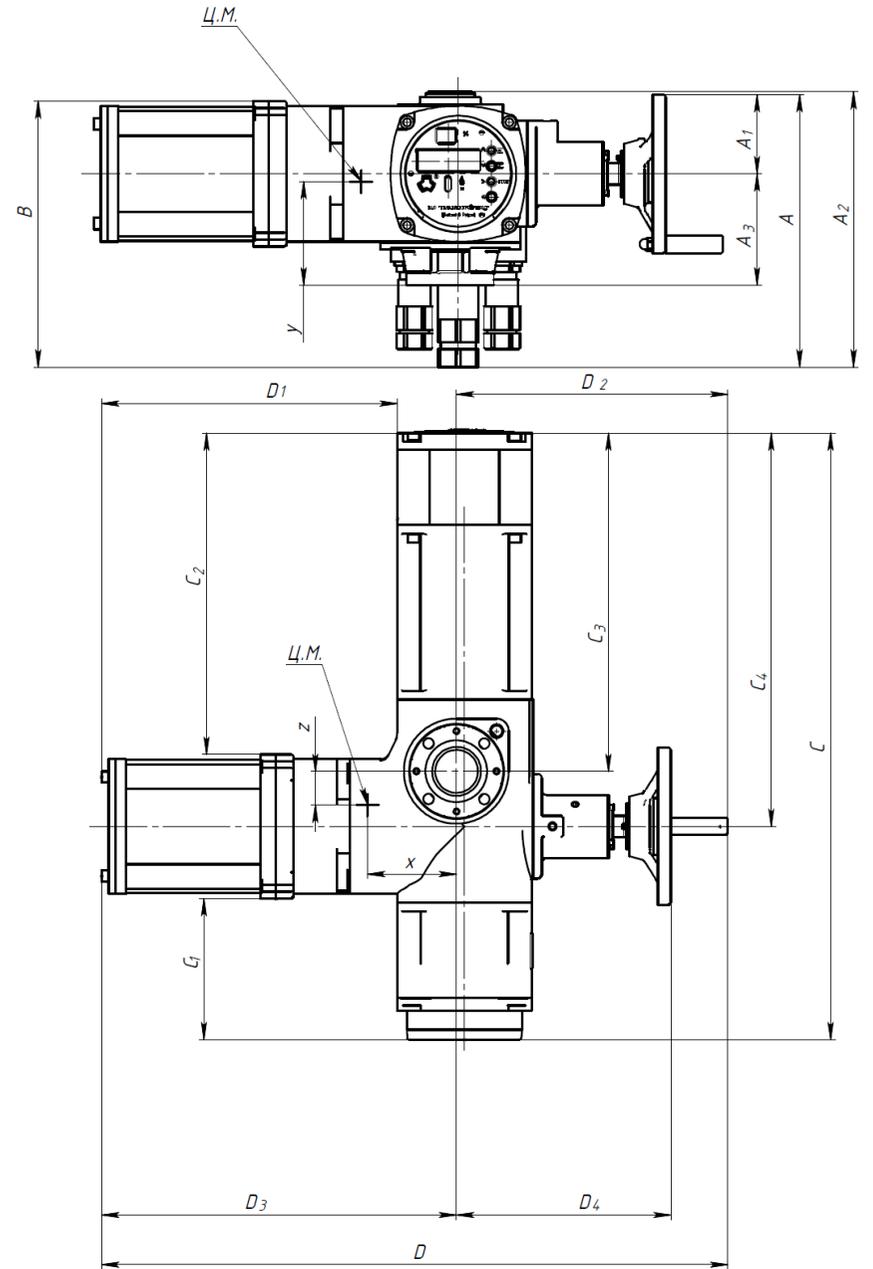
б – Габаритные размеры привода конструктивной схемы 41
